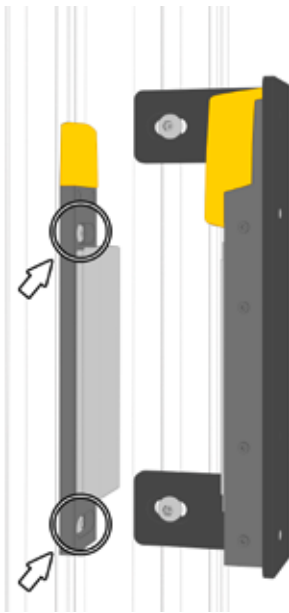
Ankerplatte am Profil der Schiebetüre anbringen, zur Prozesszuhalterung ausrichten und zur Prozesszuhalterung ausrichten. Schrauben M6 x 12 mm Torx festziehen.
